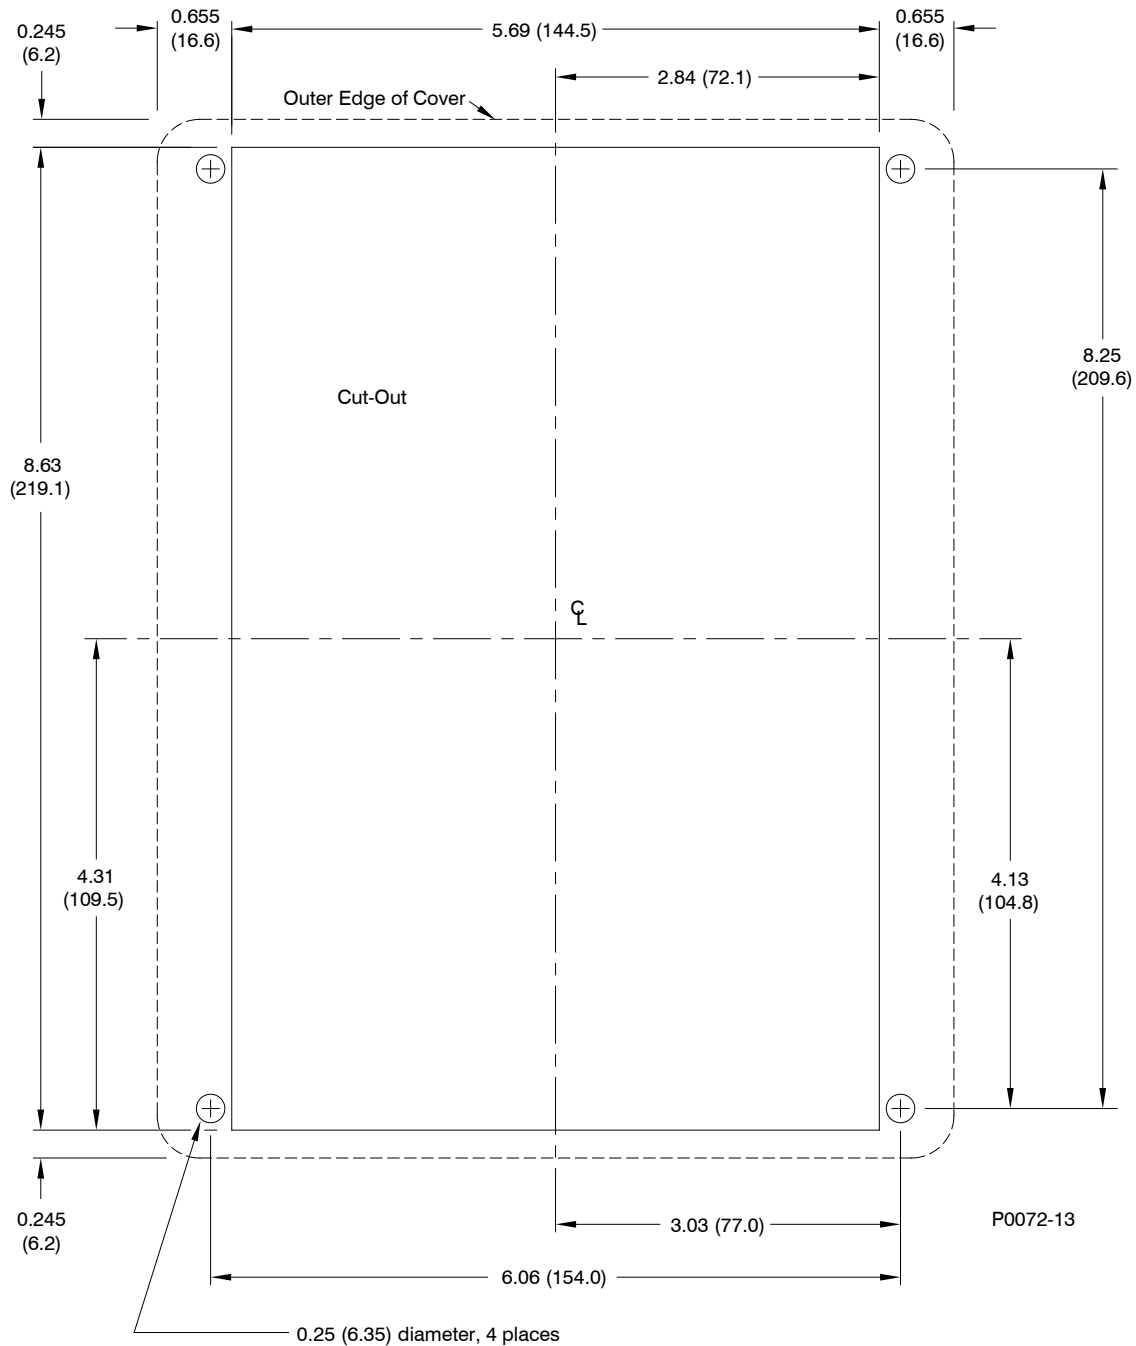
Dimensiones de cortes y perforaciones del panel
